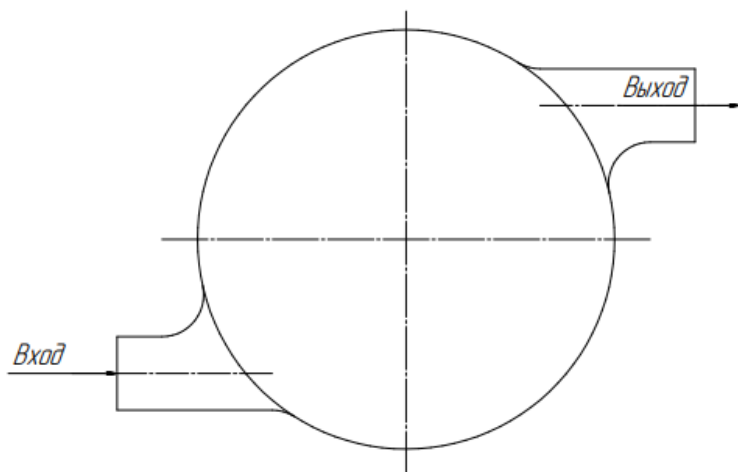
Схема входа и выхода газа пластинчато-роторного компрессора
